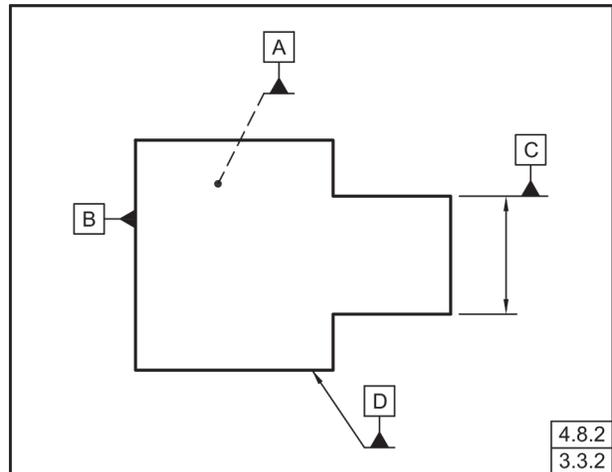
Localización de Símbolos de Elementos Datum en Elementos de Tamaño
